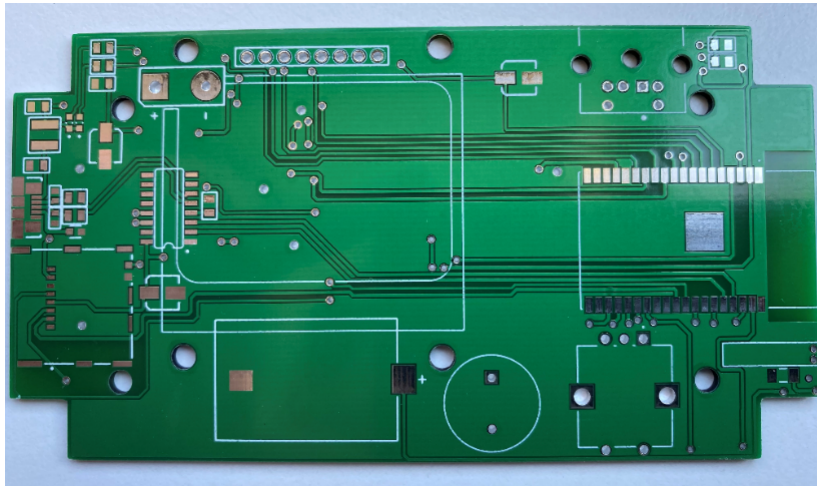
Vista superior PCB fabricada por JLCPCB
